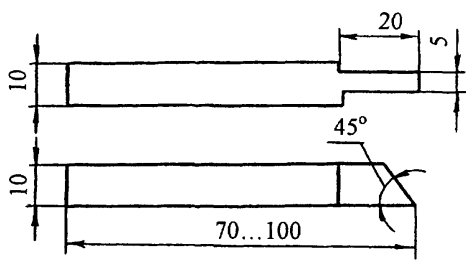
Боек для изготовления искусственных дефектов типа зарубок
